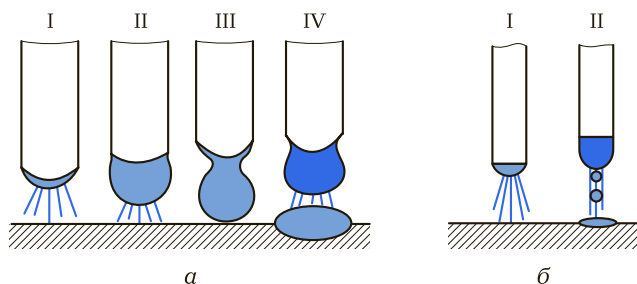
Схемы процессов переноса электродного металла в сварочную ванну:
